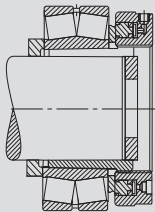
Desmontagem da Luva de Remoção com o uso de Porcas Hidráulicas
